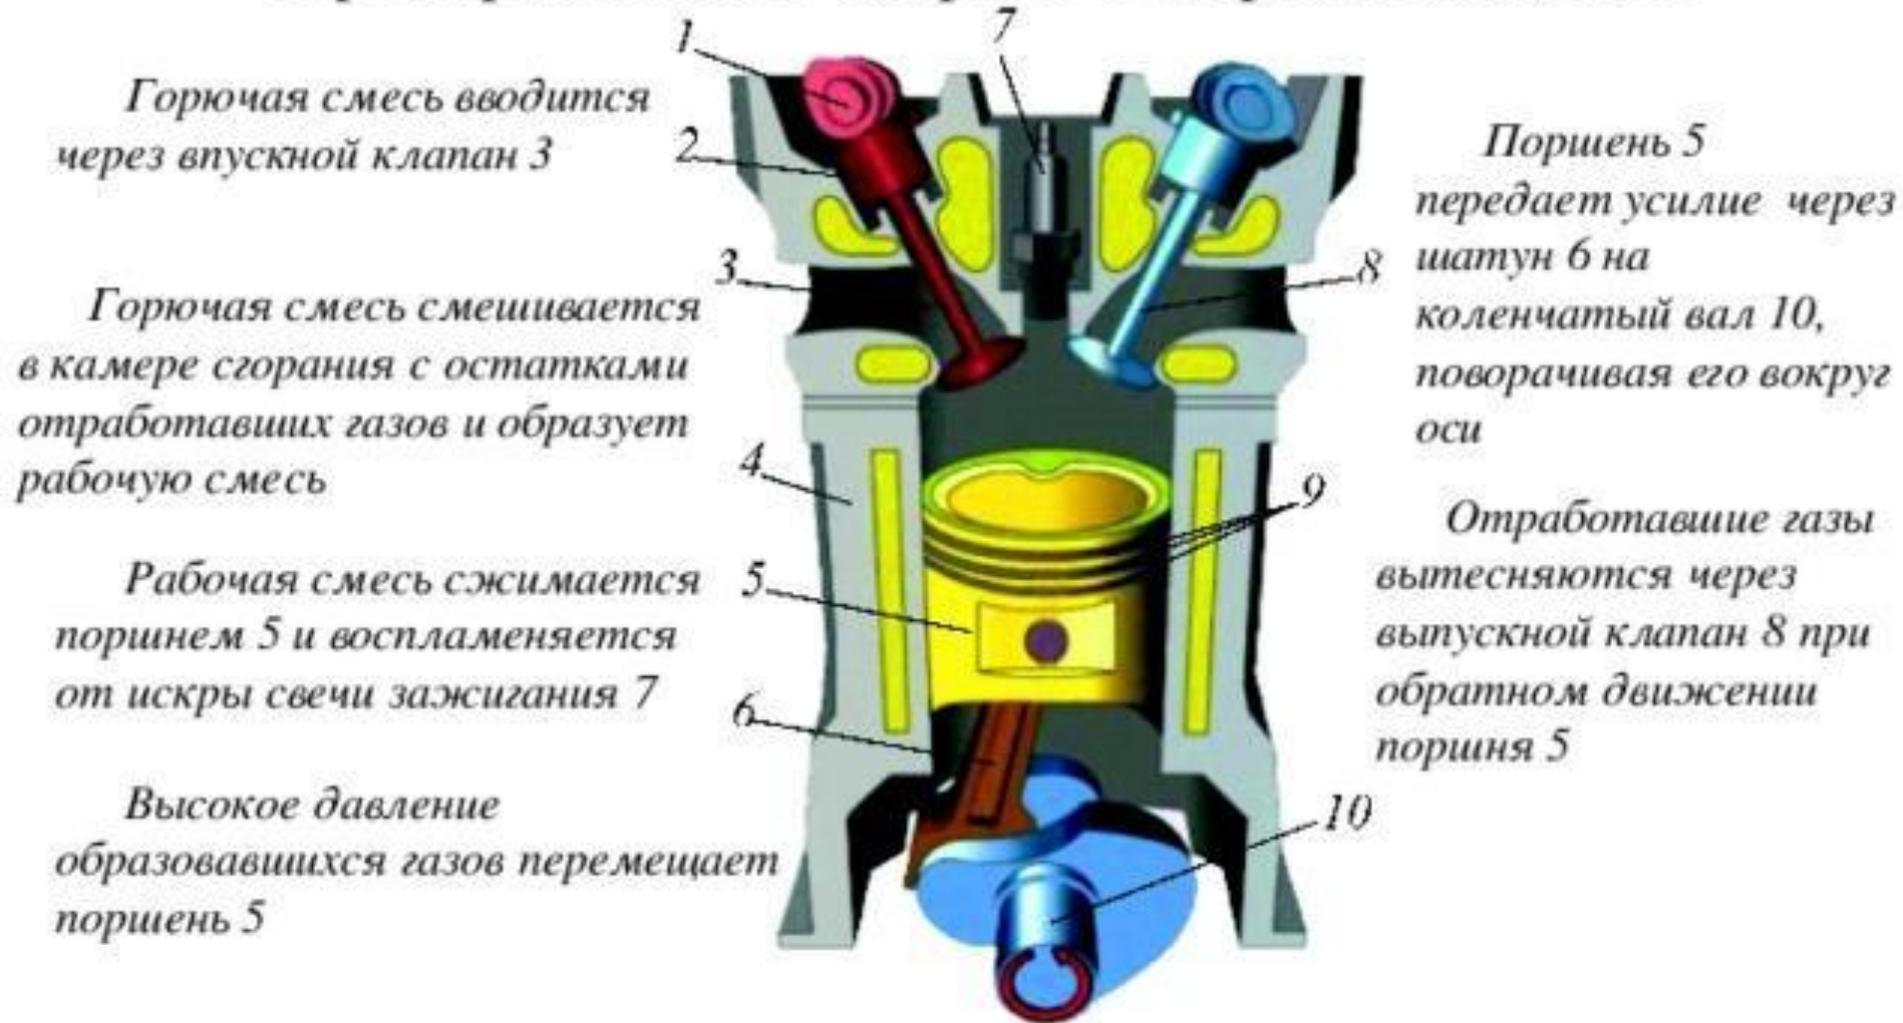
Схема четырехтактного одноцилиндрового бензинового двигателя: 1- распределительный вал; 2- толкатель; 3- впускной клапан; 4- цилиндр; 5- поршень; 6- шатун; 7- свеча зажигания; 8- выпускной клапан; 9- поршневые кольца; 10- коленчатый вал.
